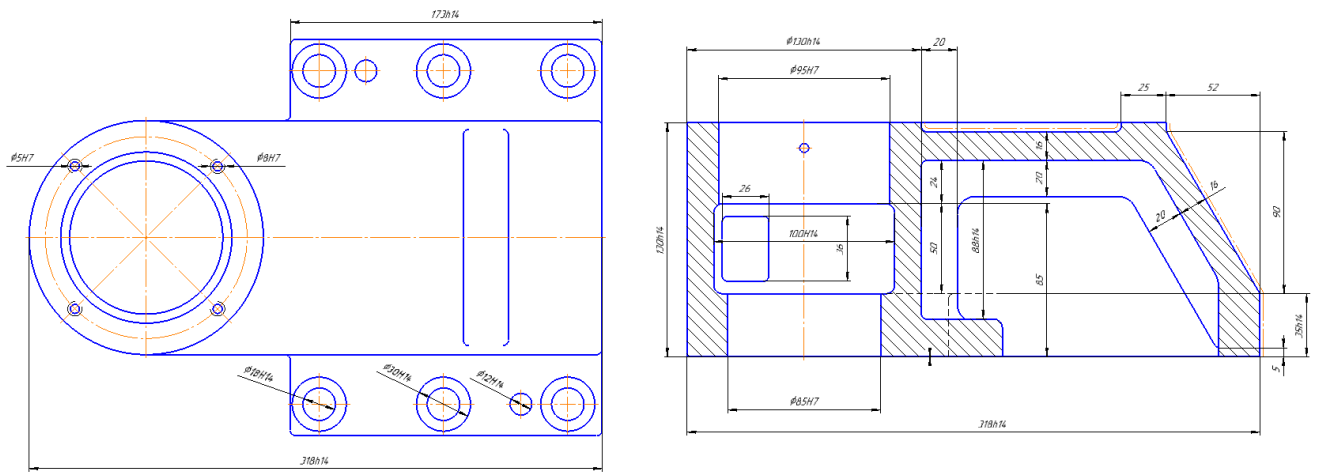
Опис поверхонь деталі типу корпус
